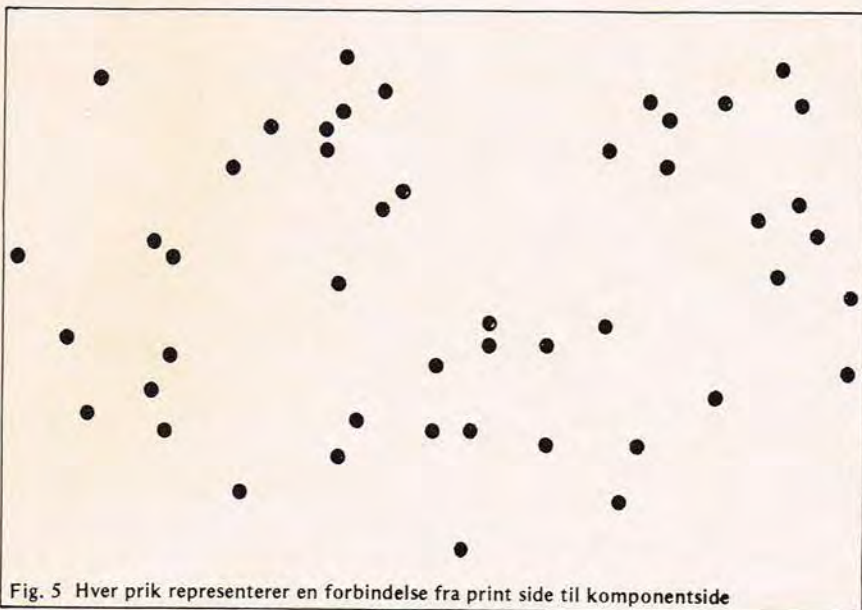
Hver prik repræsenterer en forbindelse fra print side til komponentside
